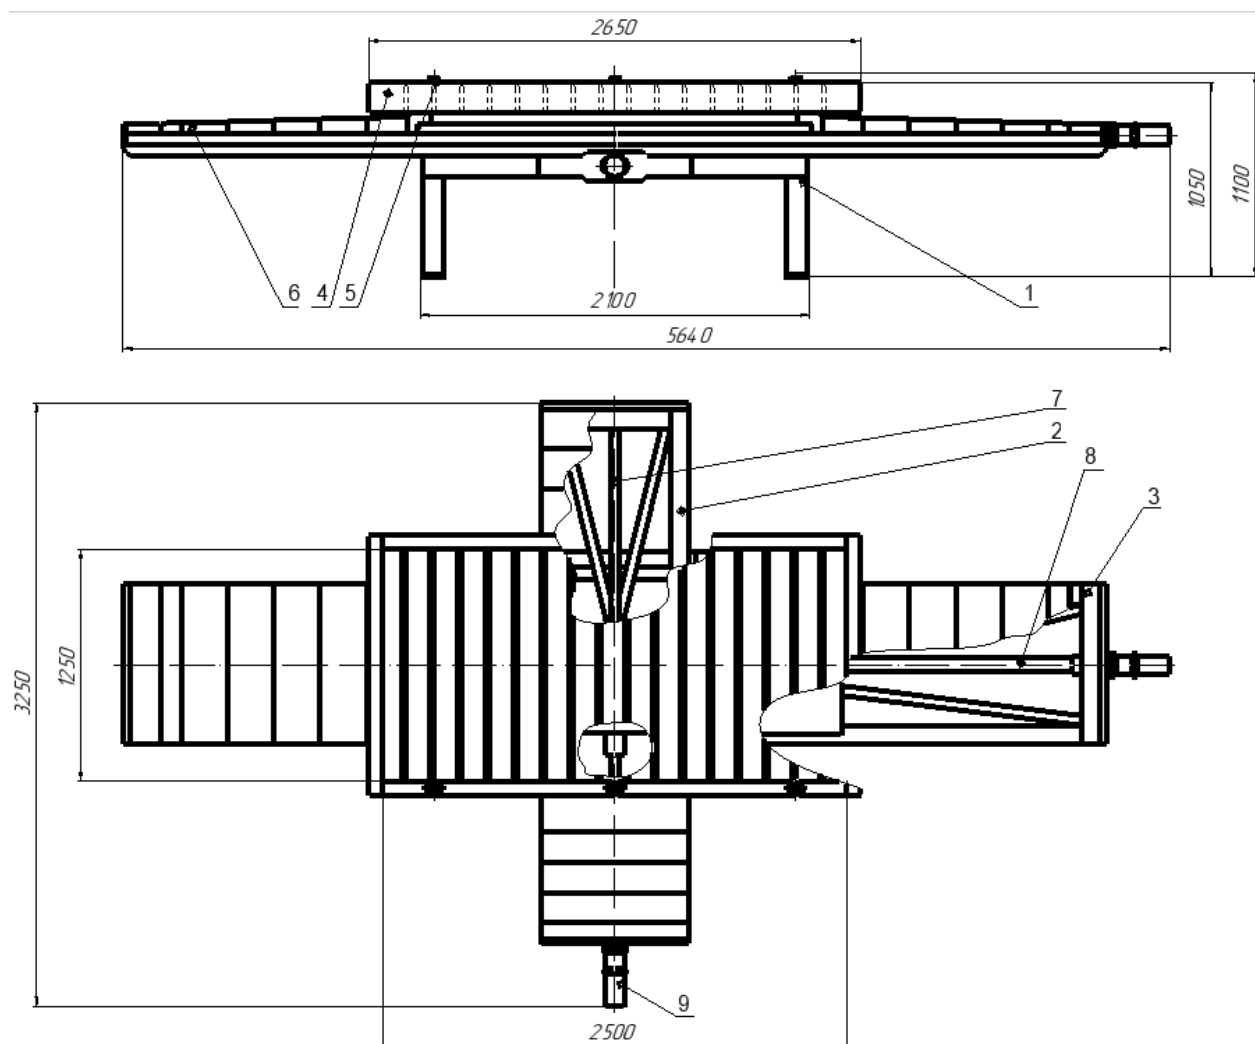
Стіл координатний: 1 – рама; 2 – механізм переміщення осі X; 3 – механізм переміщення осі Y; 4 – робочий стіл; 5 – затискач; 6 – кожух захисний; 7 – гвинтовий механізм осі X; 8 – гвинтовий механізм осі Y; 9 – кроковий електродвигун з редуктором
